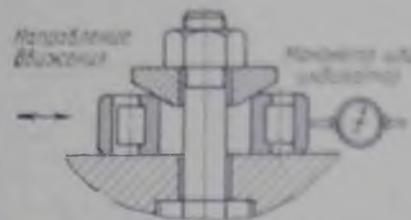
Приспособление для проверки радиального зазора в подшипниках качения
